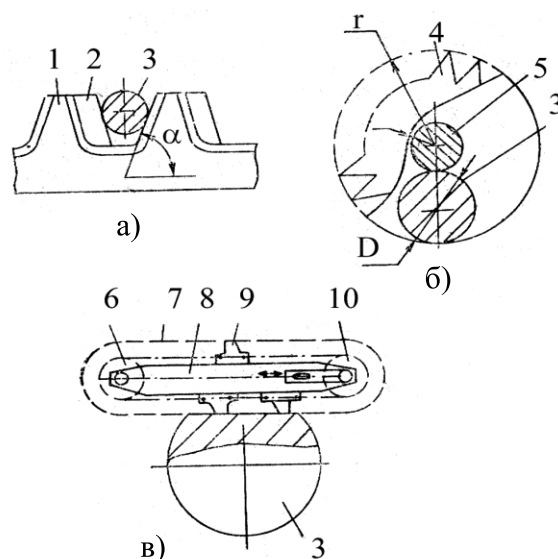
Режущие аппараты мотоинструмента: а – сегментного типа; б – пильный диск; в – пильная цепь: 1 – верхний нож; 2 – нижний нож; 3 – ветка; 4 – зубцы диска; 5 – вал диска; 6 – ведущая звездочка; 7 – цепь; 8 – пильная шина; 9 – режущее звено цепи; 10 – натяжная или направляющая звездочка
